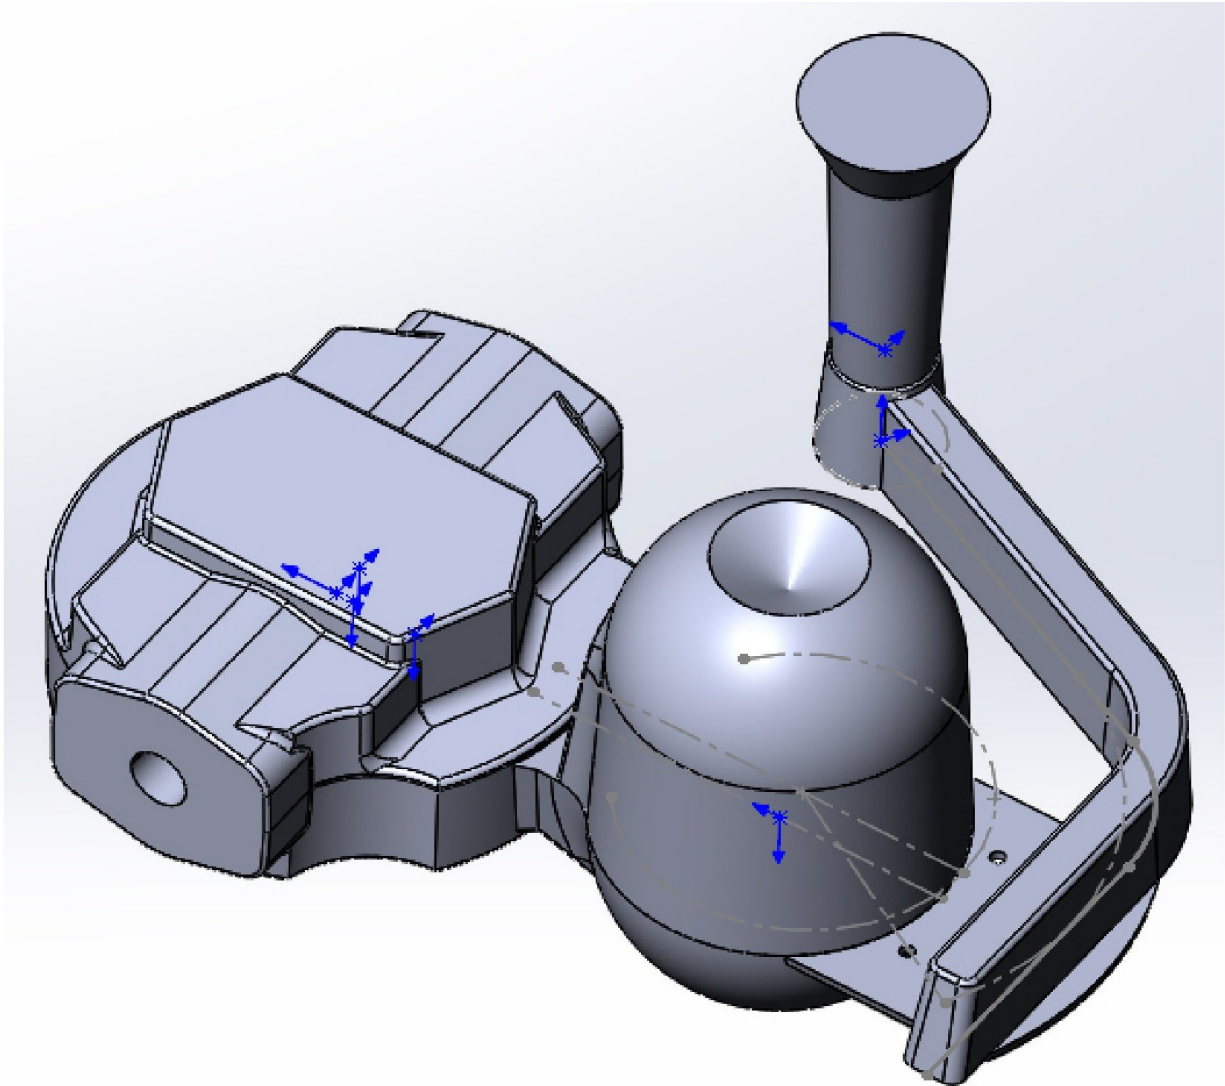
3Д зборка компоновки вилівка з ливниково-живильною системою
